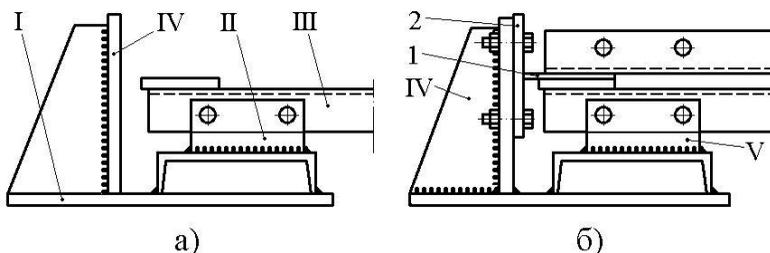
Схемы фиксирования положения монтажных отверстий в опорных узлах ферм
